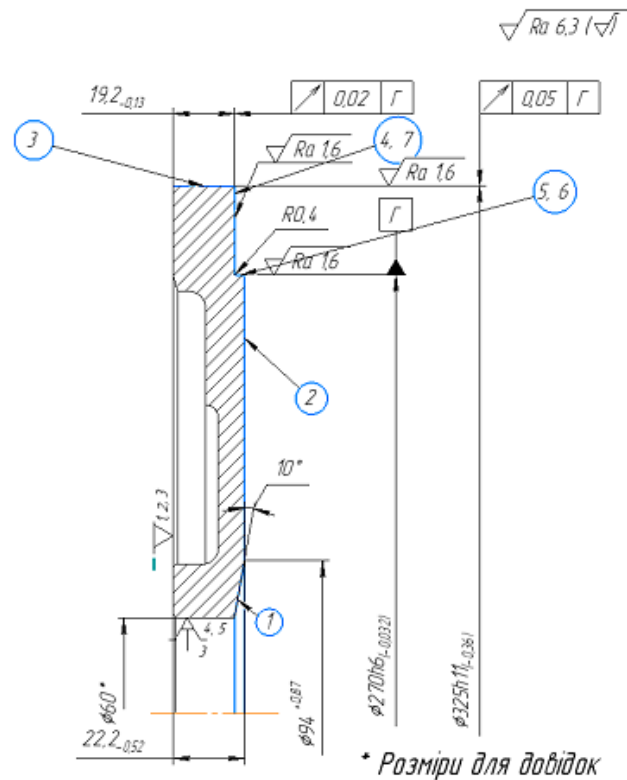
Ескіз деталі для нормування операції 045
